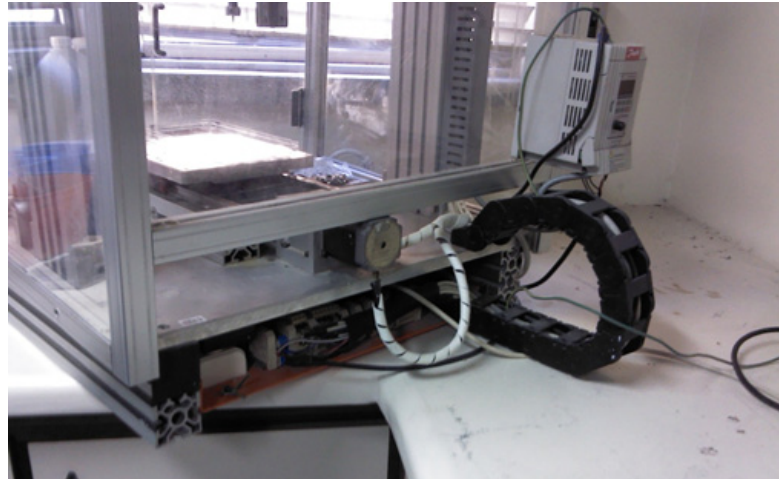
Fresadora CNC compacta montada com estrutura em perfil de alumínio.
